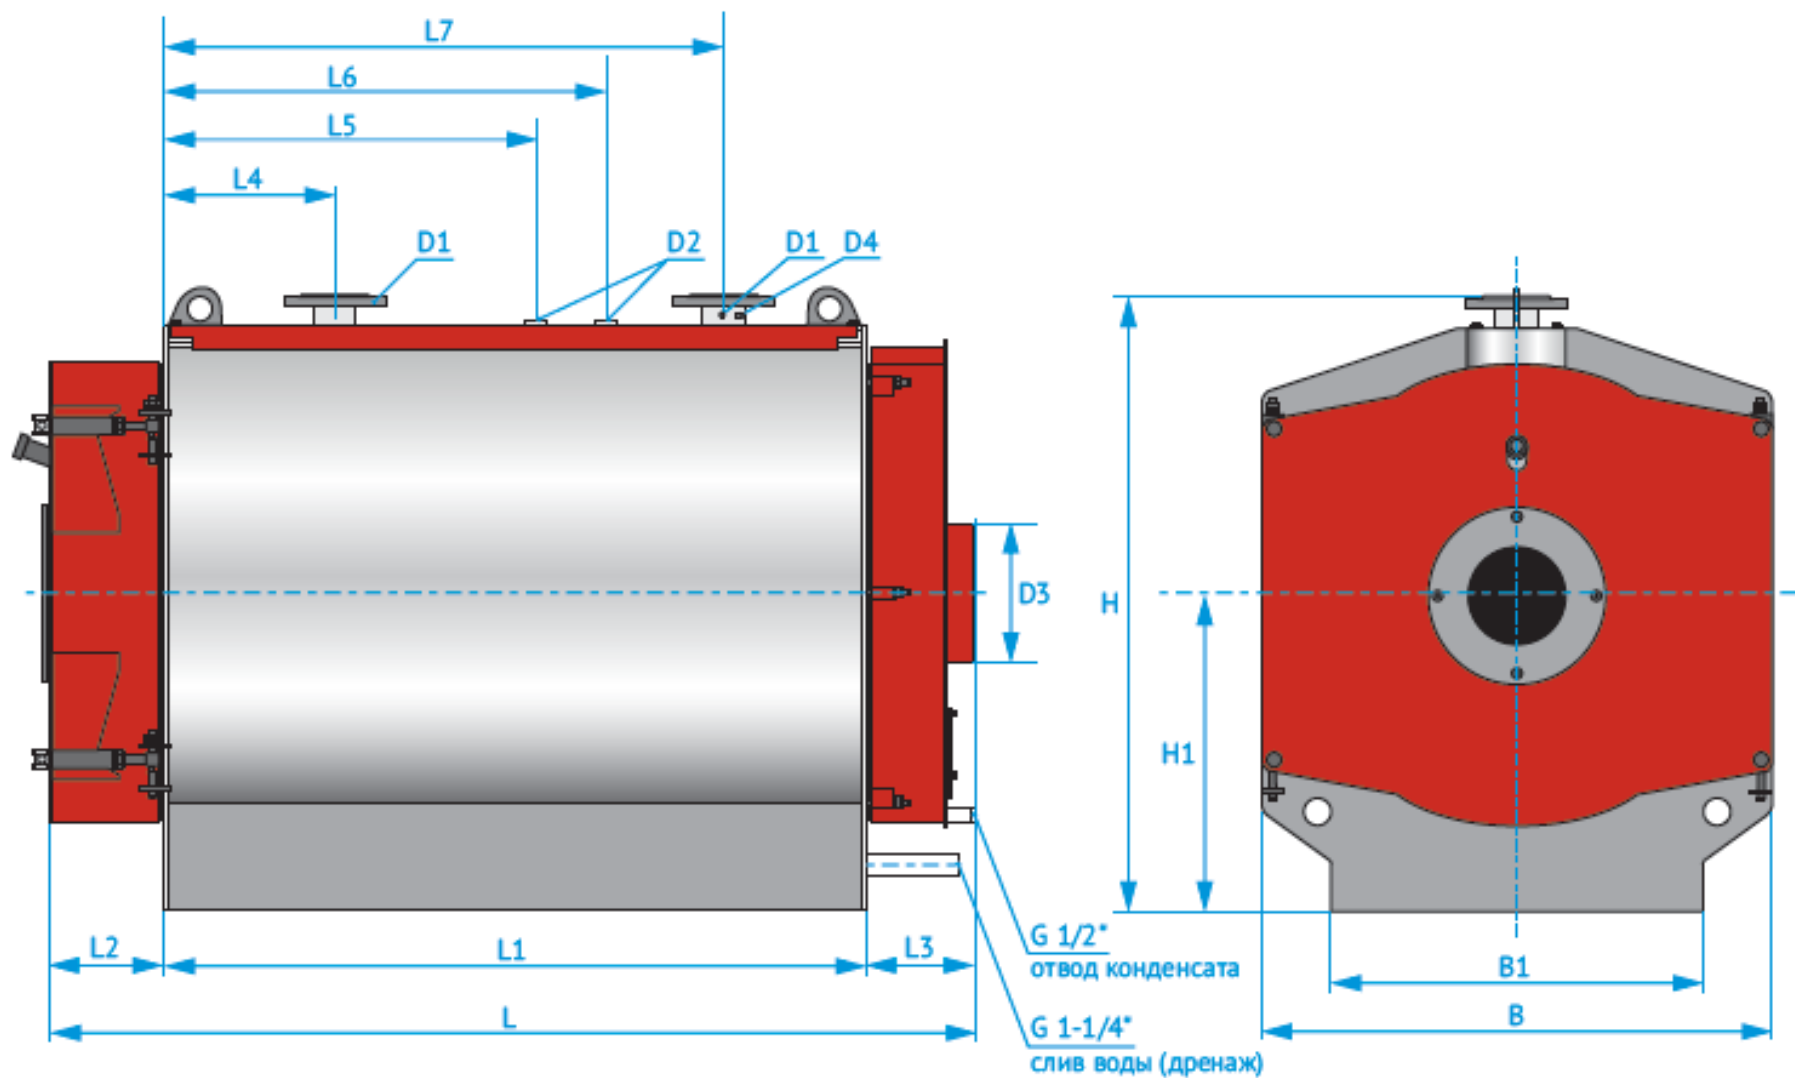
Габаритные и присоединительные размеры котлов WL400-1250
